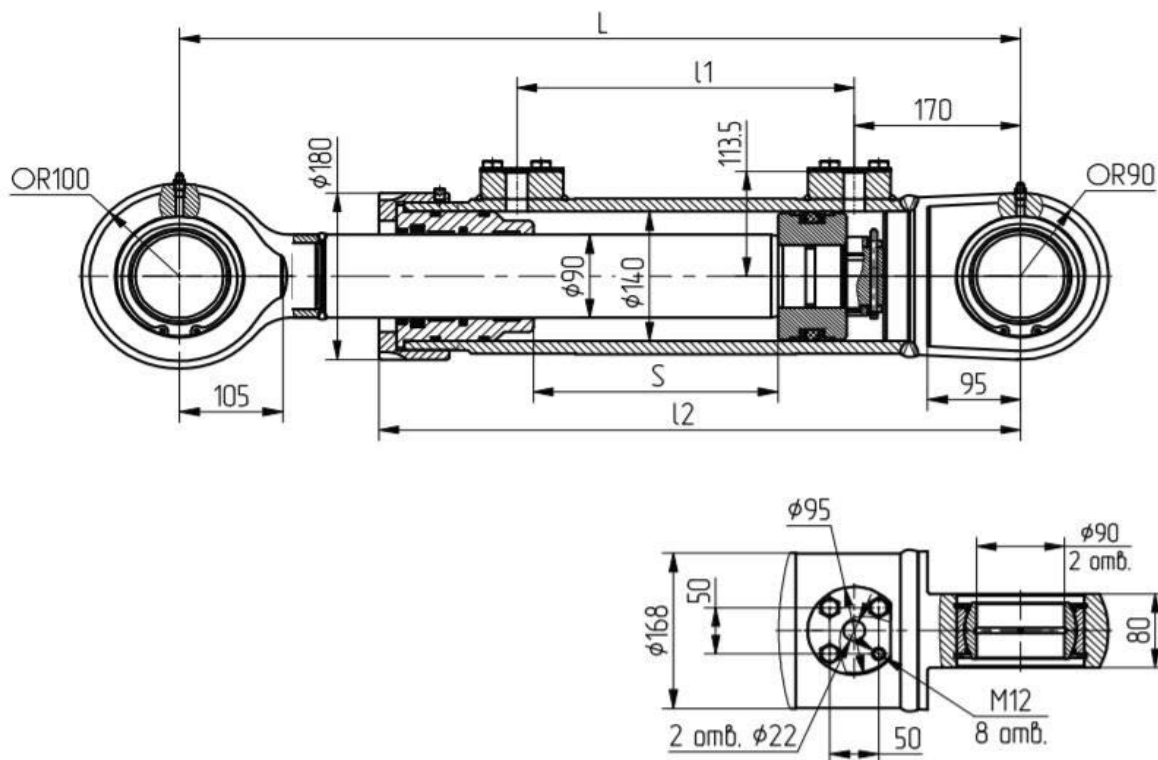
Гидроцилиндр КГЦ491.140-90-1000
